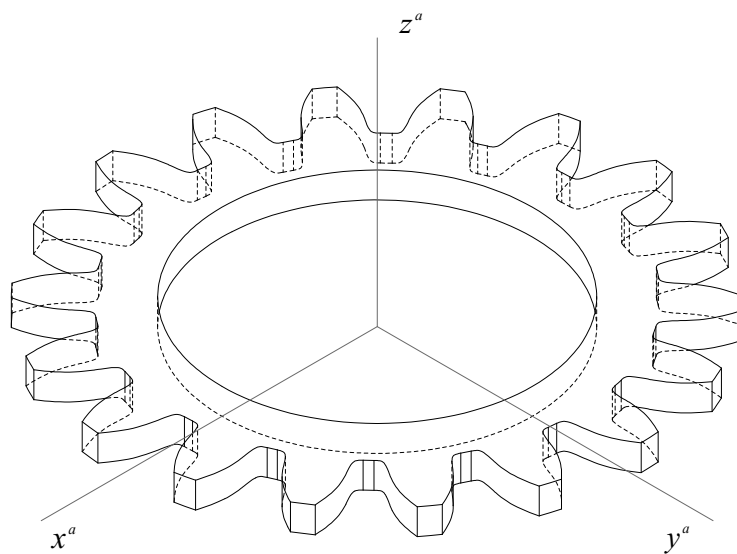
ozubené kolo v planometrii, 1. Zadání
